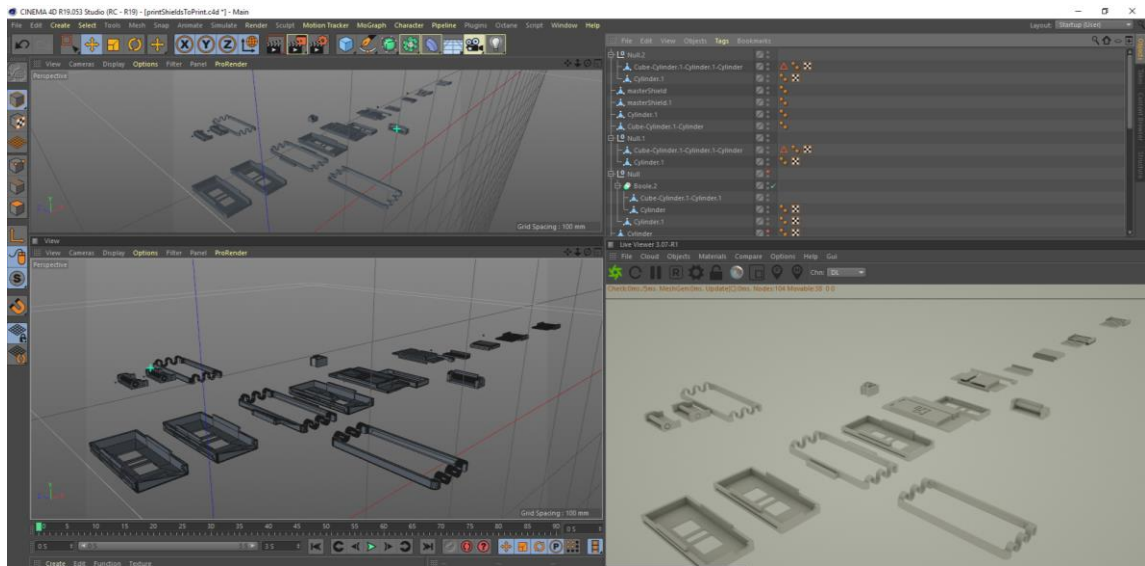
3D de proposta de design para os módulos principal, incluindo sistema de fixação com mola.
